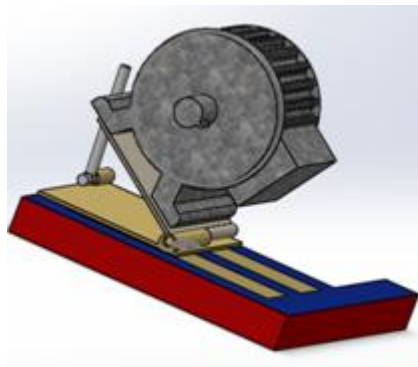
2 Diseño de la base del Motor, Tensor y Motor
